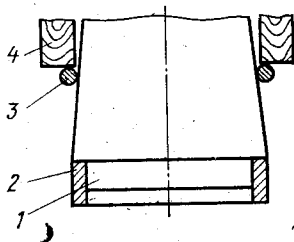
Приспособление для монтажа проволочных уплотнителей:
